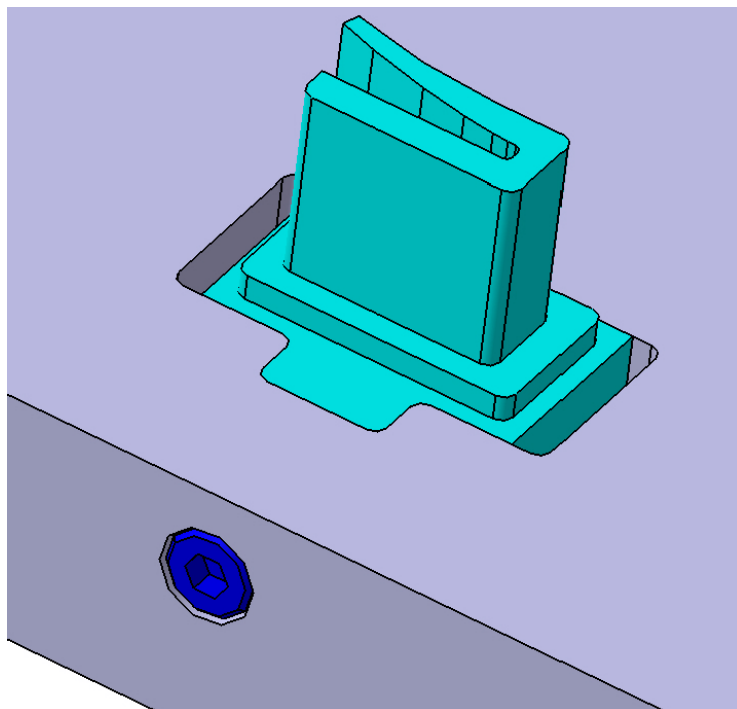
Detail- drážka pro uchycení krajního zobáčku
